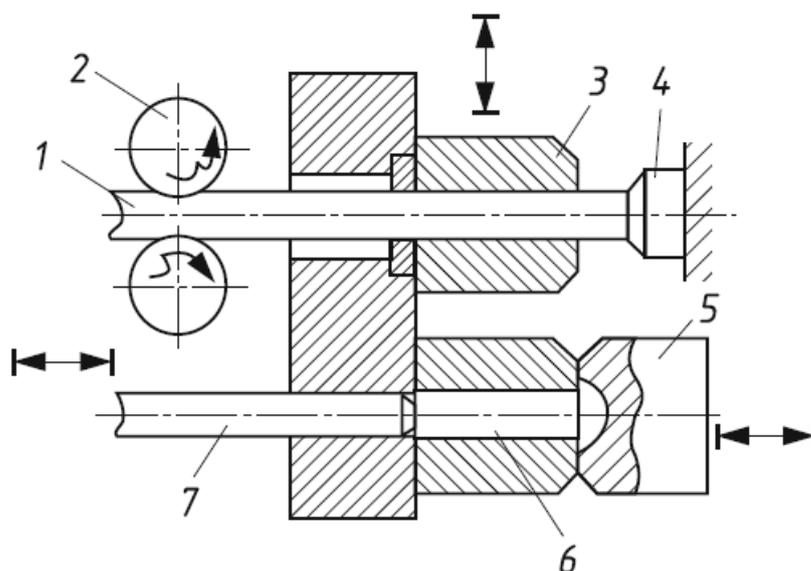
Схема высадки головки винта на штамповочном автомате
